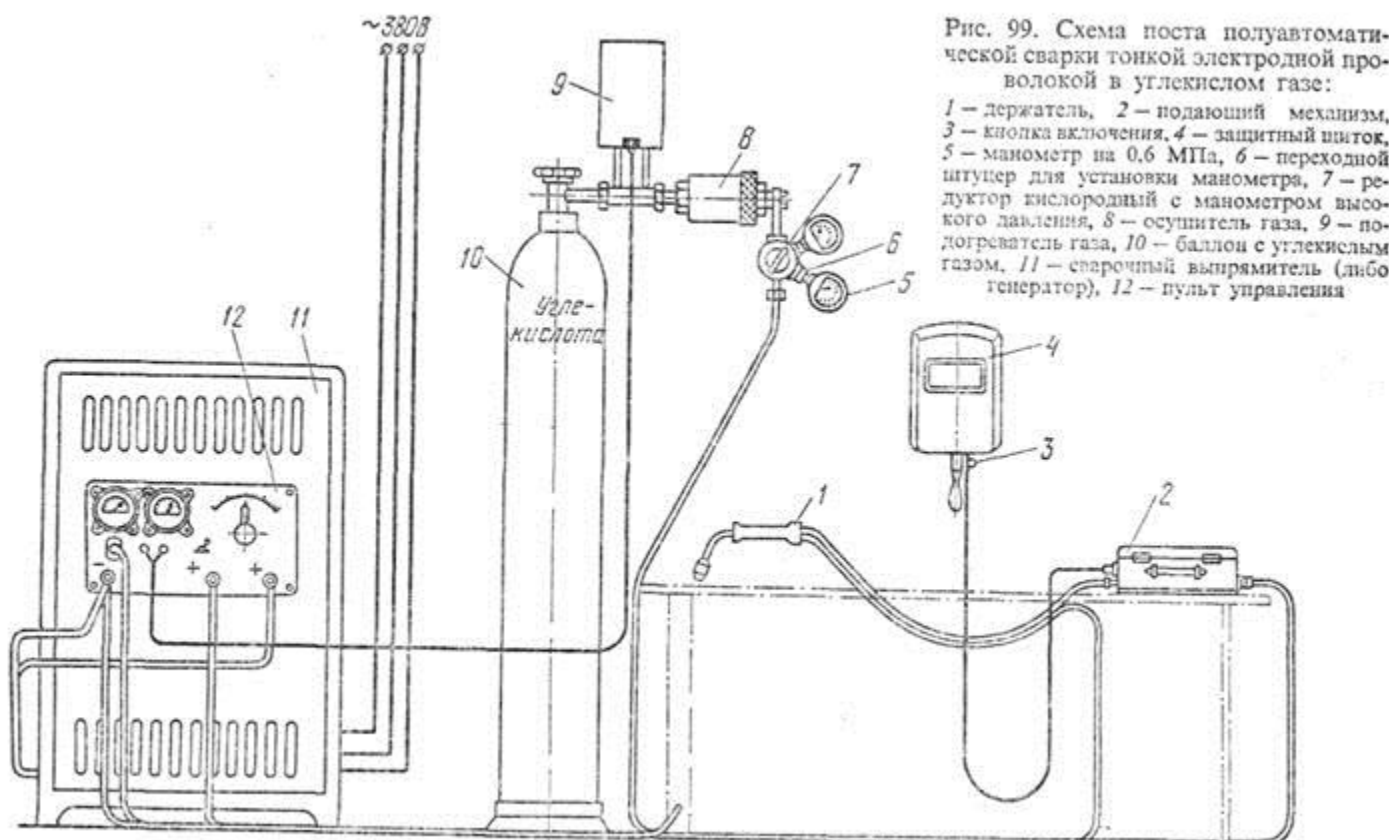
Схема поста полуавтоматической сварки тонкой электродной проволокой в углекислом газе:
